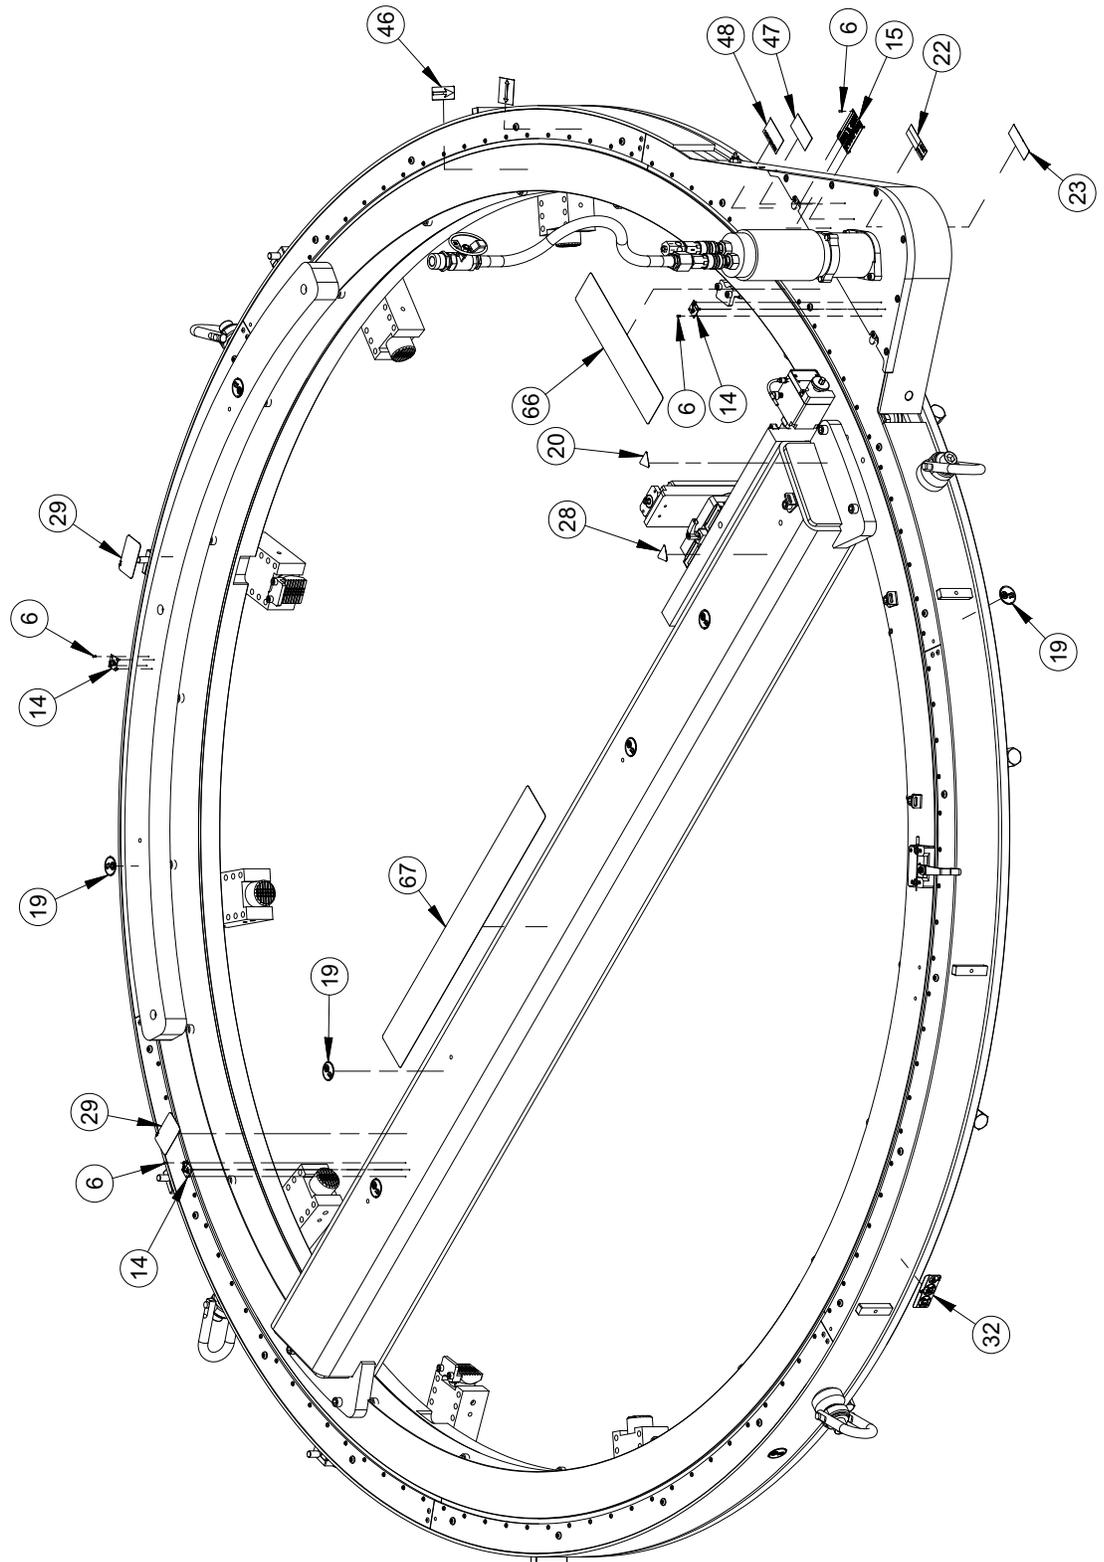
ODF100 SPEED FACER EMBLEMES DES ÉTIQUETTES (RÉF. 94790)
